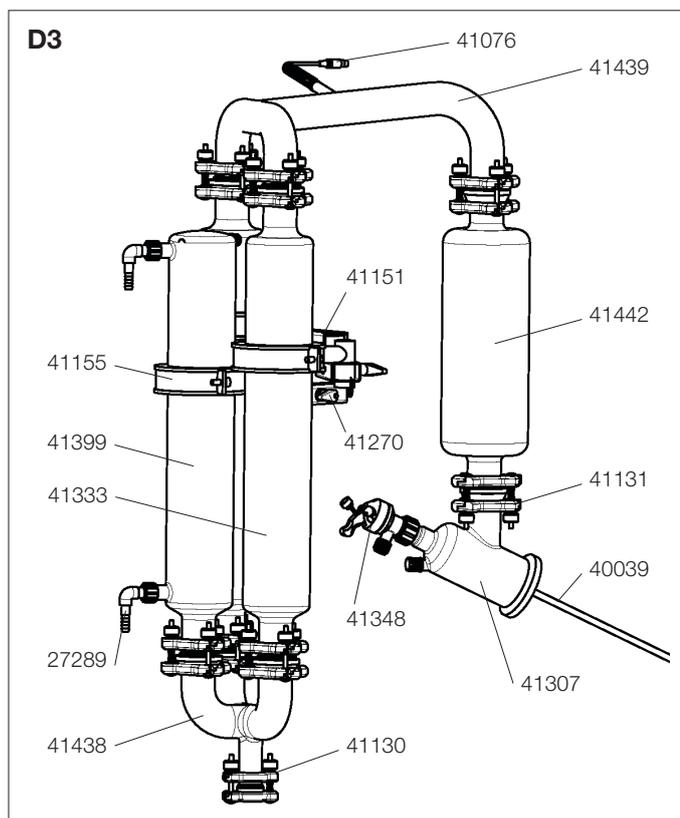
Piezas de repuesto, construcción de piezas de vidrio ,descendente'
